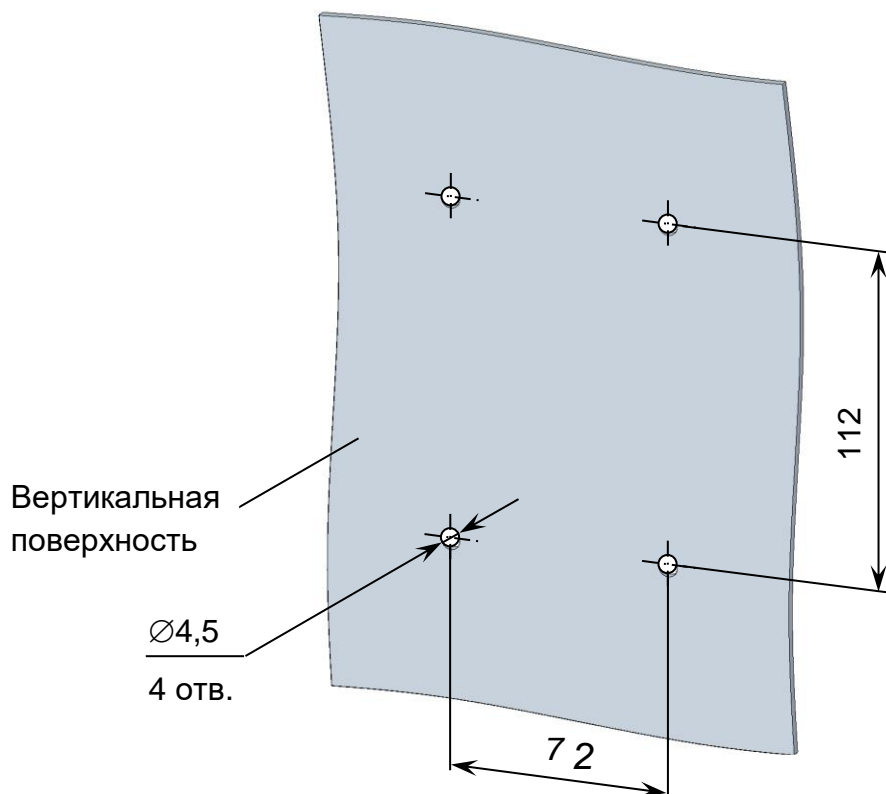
Расположение и размер отверстий для крепления источника питания ИП-1002
